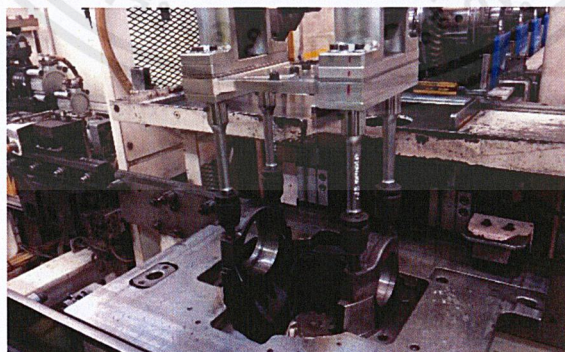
ปัญหา Socket มีขนาดยาว และหัว Socket ไม่จับ Bolt
